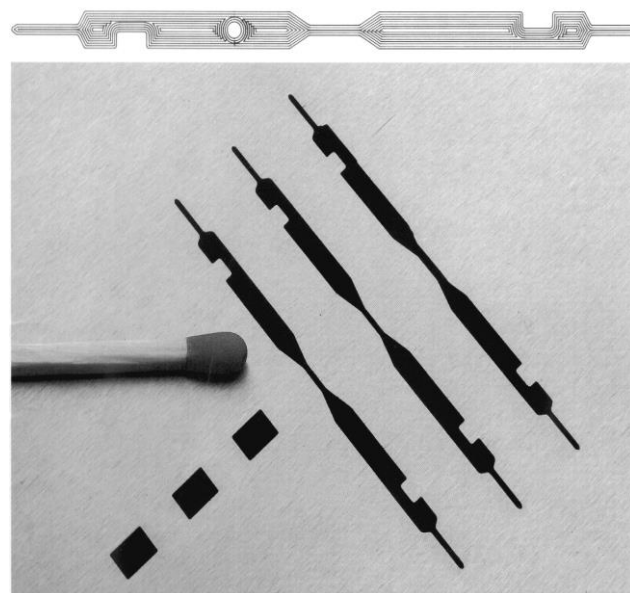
Пример доработки переходных участков заготовки после фрезерования
